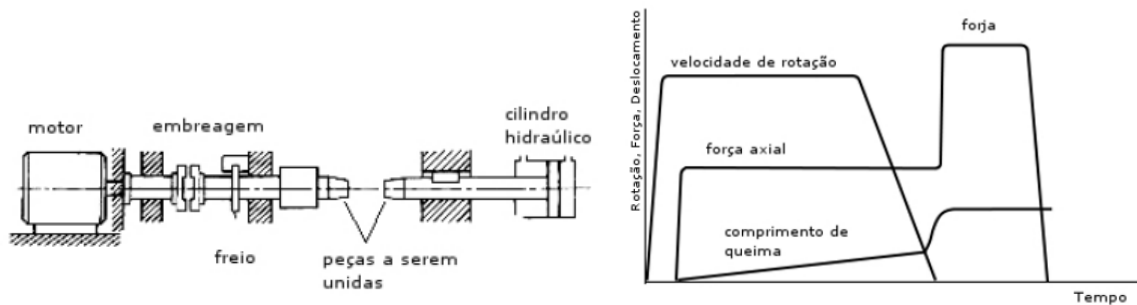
Equipamento de soldagem por fricção [Fonte: ALVES, 2010]
